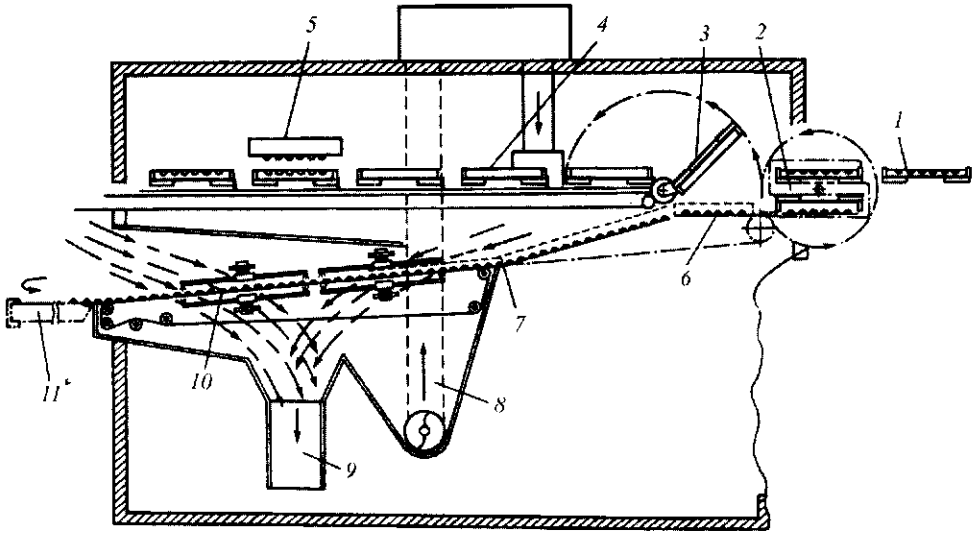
Отливочный агрегат НИД типа М301Р
